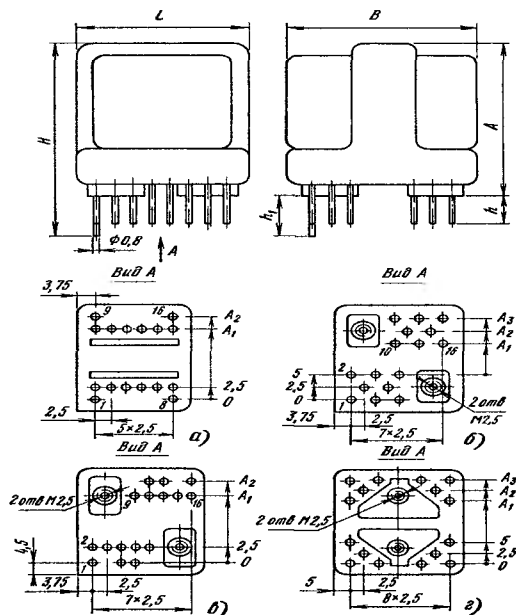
Общий вид и габаритные размеры трансформаторов типа ТП с частотой питающей сети 1 000 Гц
